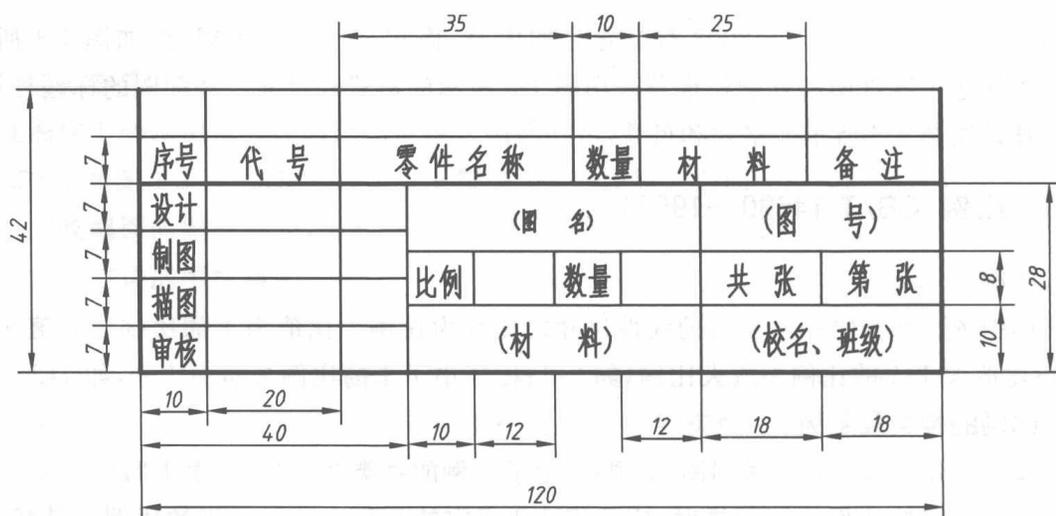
作业中装配图所用标题栏及明细表的尺寸与格式
